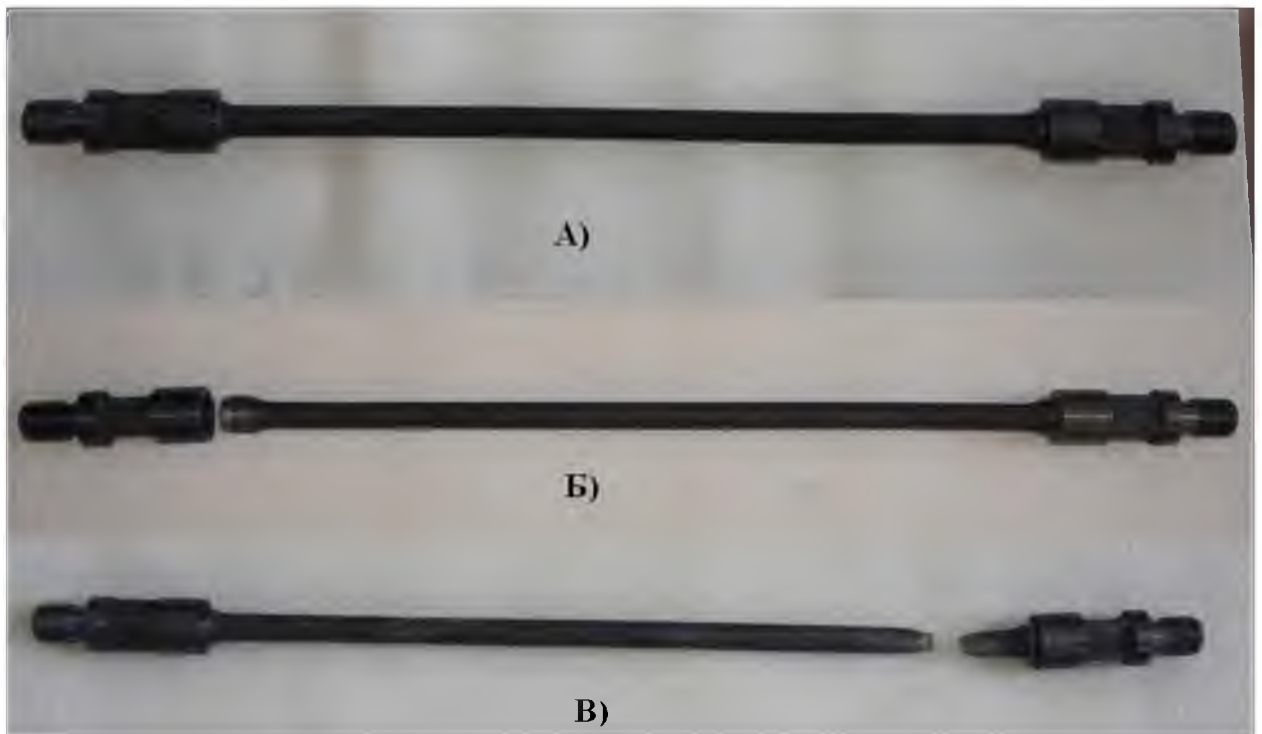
а – опытный образец штанги; 4.2 б – образец штанги, изготовленный по третьему варианту конической резьбы; 4.2 в – образец штанги, разрушенный по телу при нагрузке 22 т.с.
